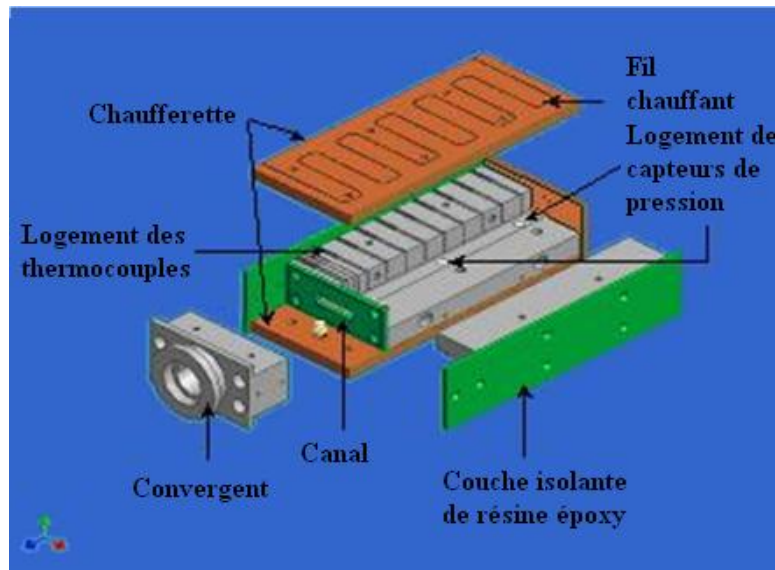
Dessin éclaté de la filière d'extrusion
